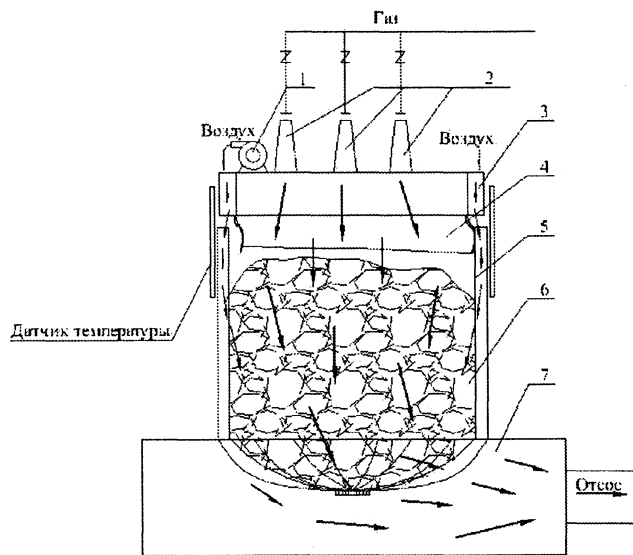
Схема работы бадьи-термоса: 1 — продувочный вентилятор; 2 — горелки; 3 — коллектор обдува; 4 — огнестойкая завеса; 5 — вставка; 6 — нагреваемая шихта; 7 — корпус стнда
